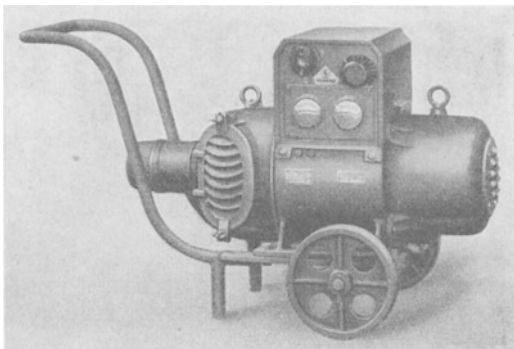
Fahrbarer Eingehäuseumformer mit Querfelddynamo.
